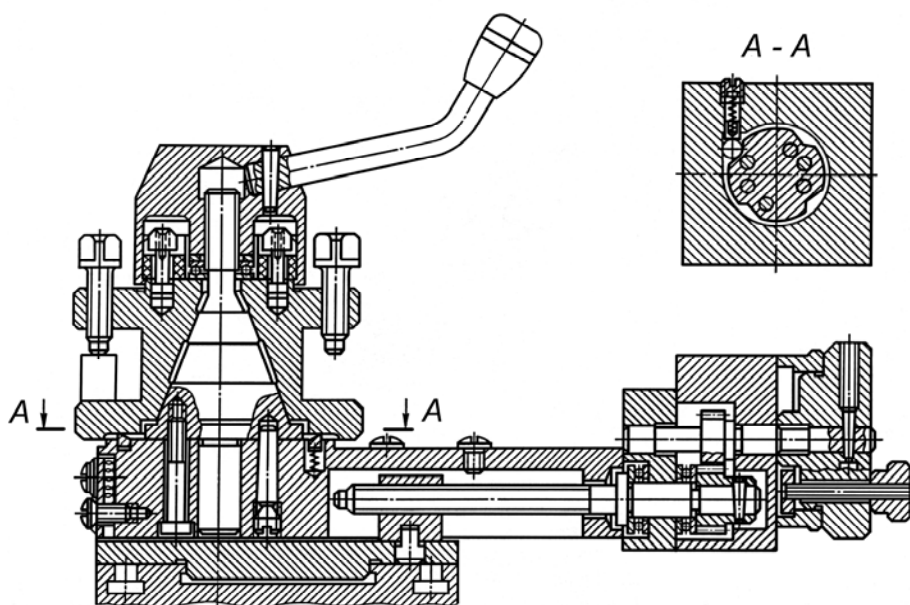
Верхний суппорт с 4-х позиционным резцедержателем
